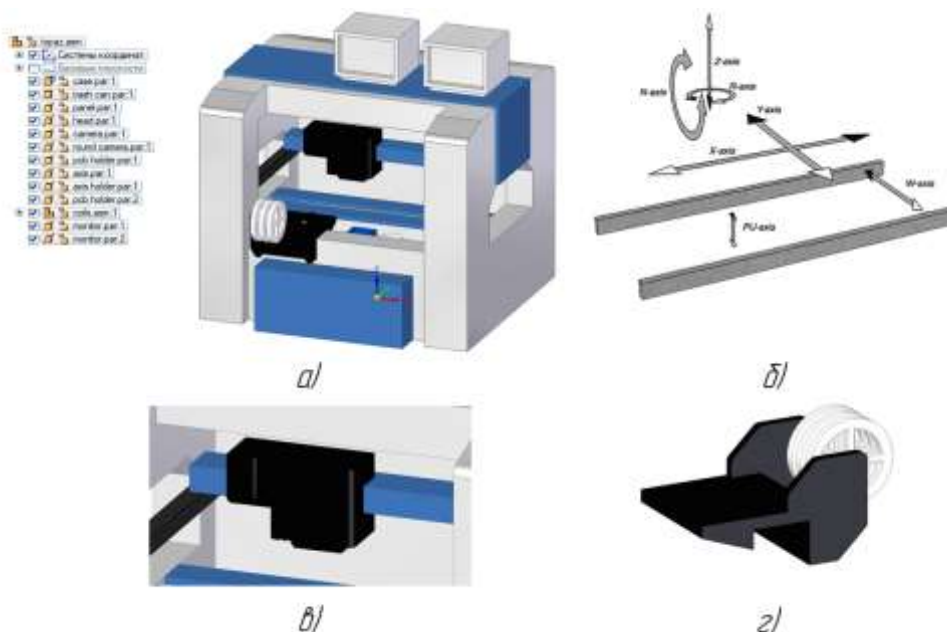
цифровая модель гибкого сборочного автомата Toraz компании Philips/Assembleon: а) модель сборки в САПР Solid Edge; б) схема перемещения исполнительных механизмов по осям; в) модель сборочной головки; г) модель блока питателей с катушками
